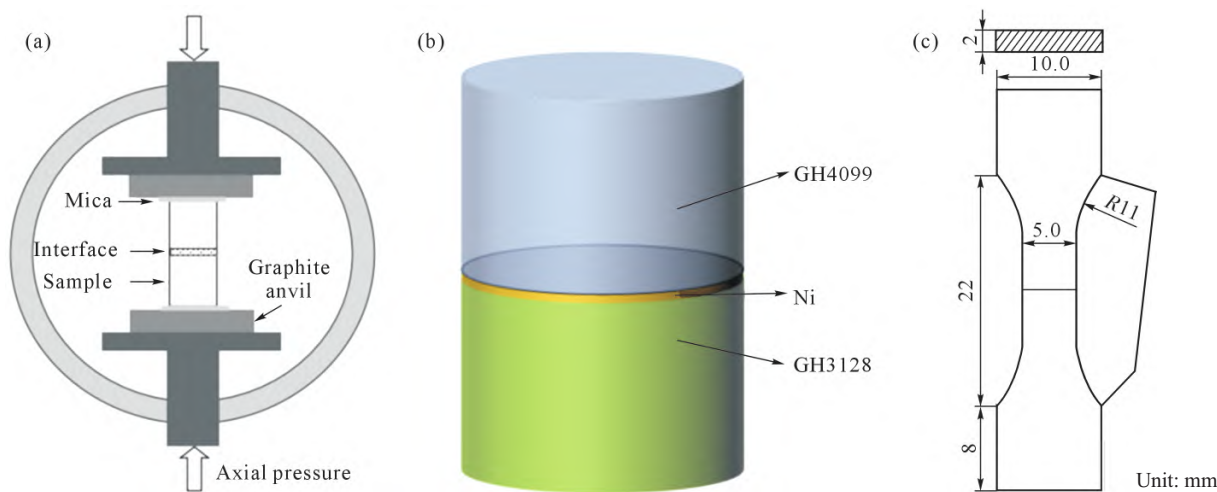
试样装配示意图与接头拉伸试样尺寸示意图: (a) 焊接工装示意图; (b) 装配示意图; (c) 拉伸试样的几何形状
